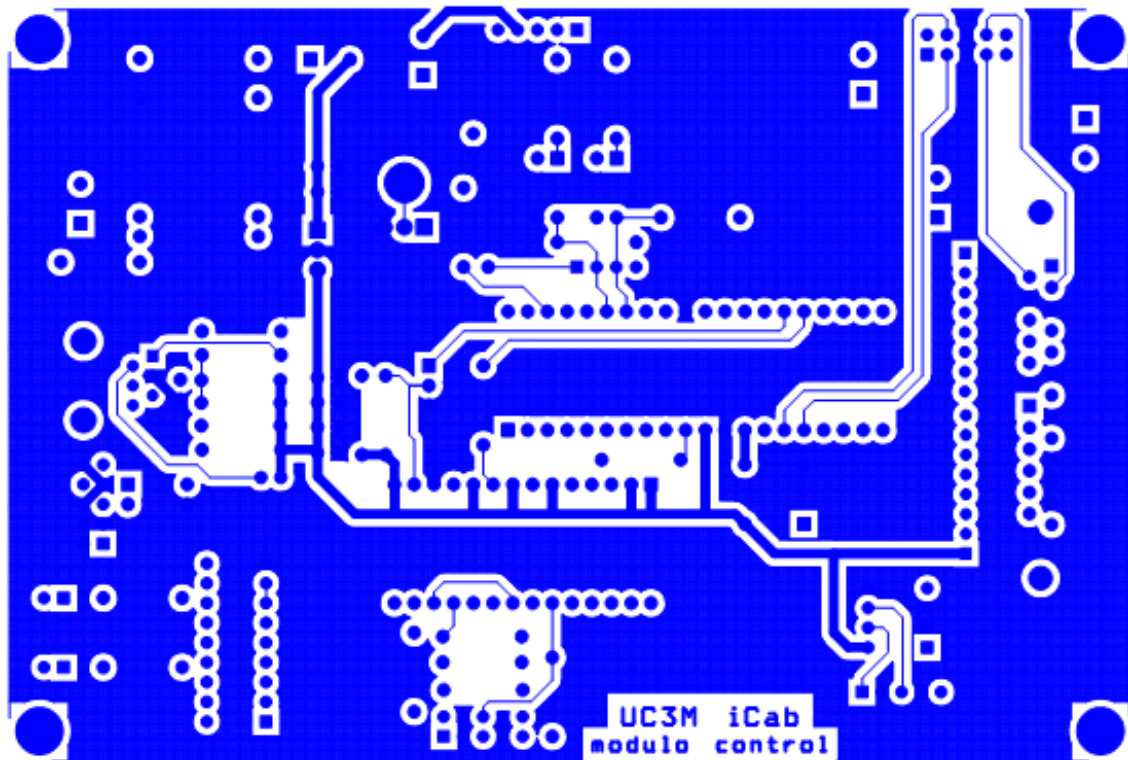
Placa del módulo de control Layout final. Capa TOP
